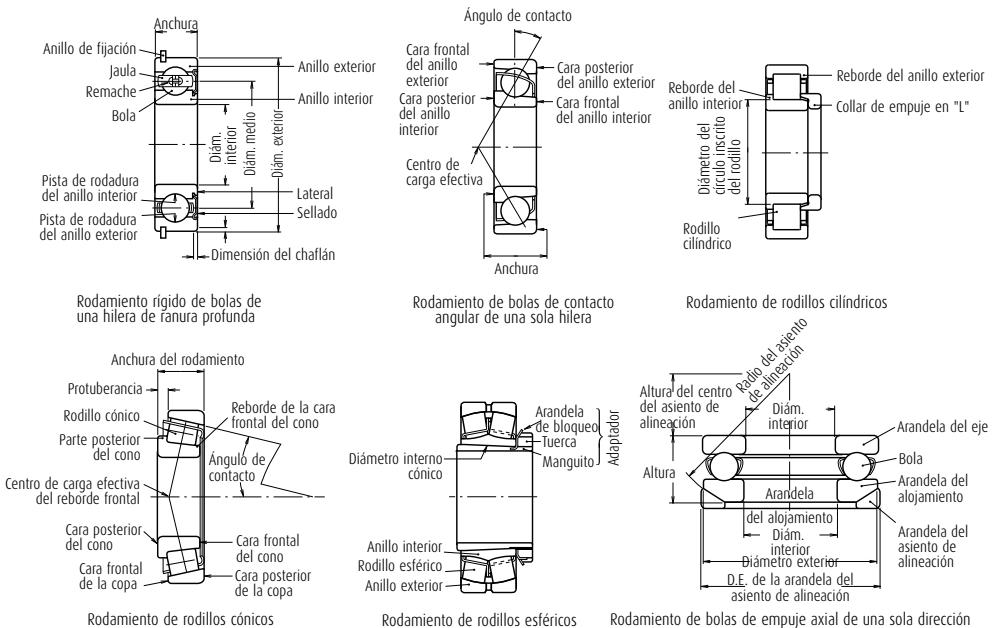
Nomenclatura para las partes de los rodamientos
